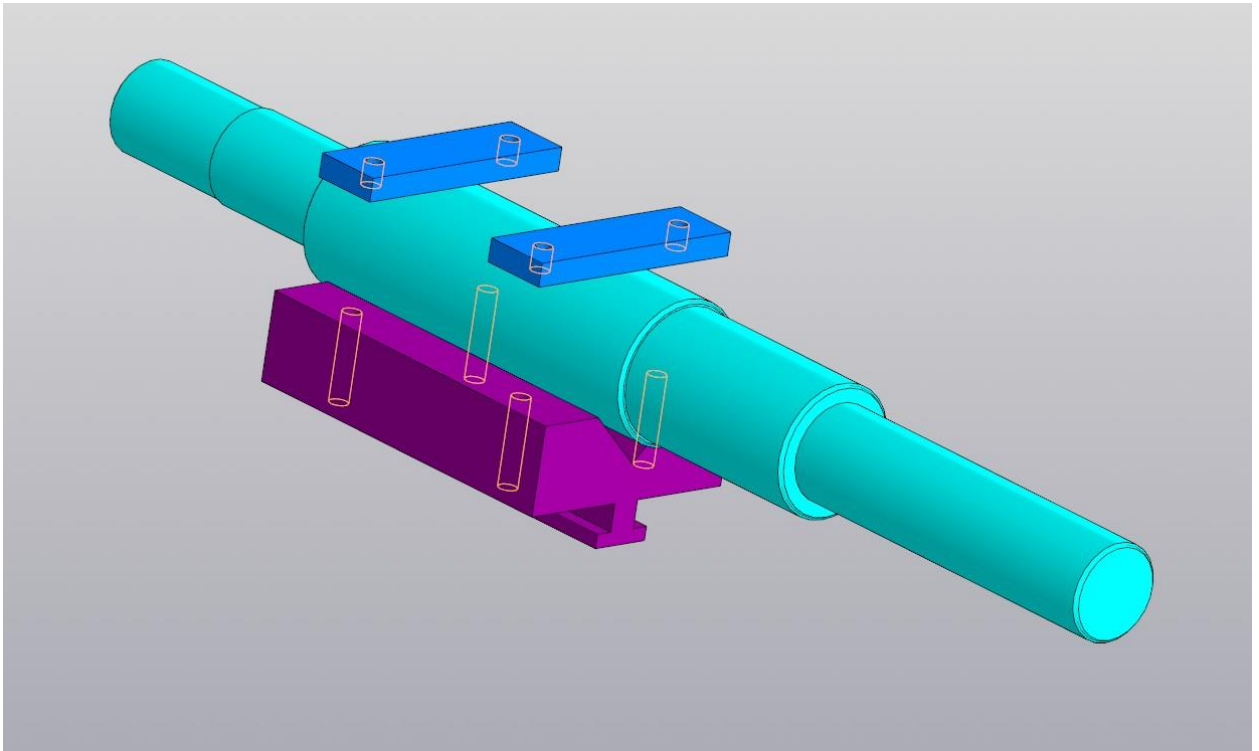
3D – модель приспособления для фрезерной операции
